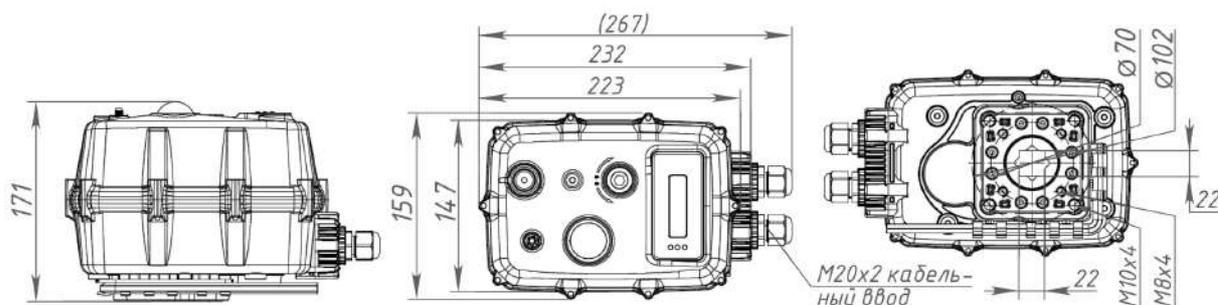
Габаритные размеры электроприводов Motorvalve серий Smart S200 и S400.
